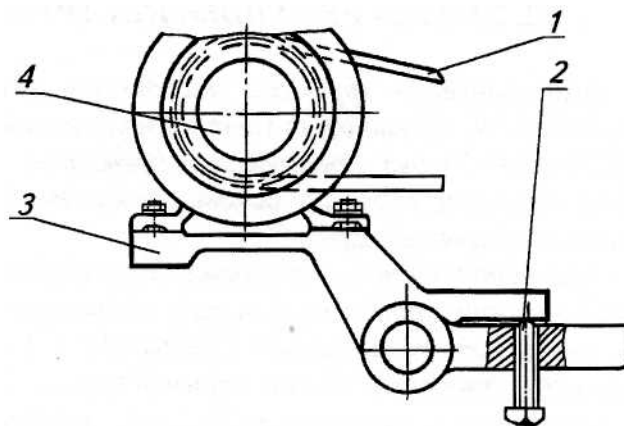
Устройство для натяжения ремней вертикальных суппортов.
